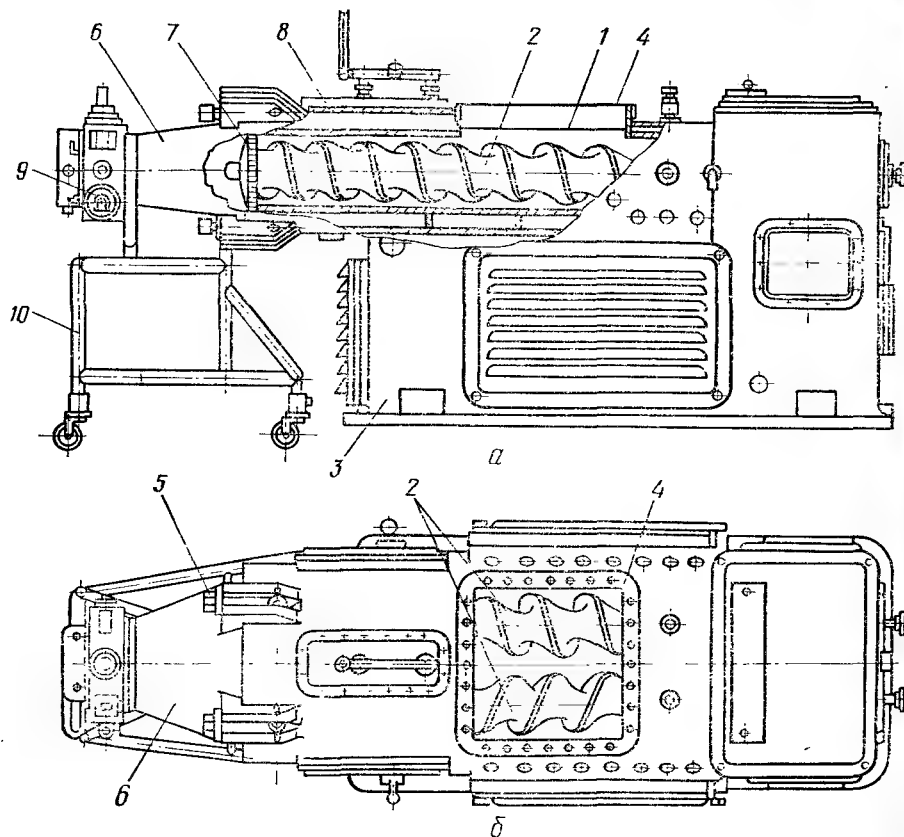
Одноступенчатый двухвинтовой шнек-пресс для хозяйственного мыла:
